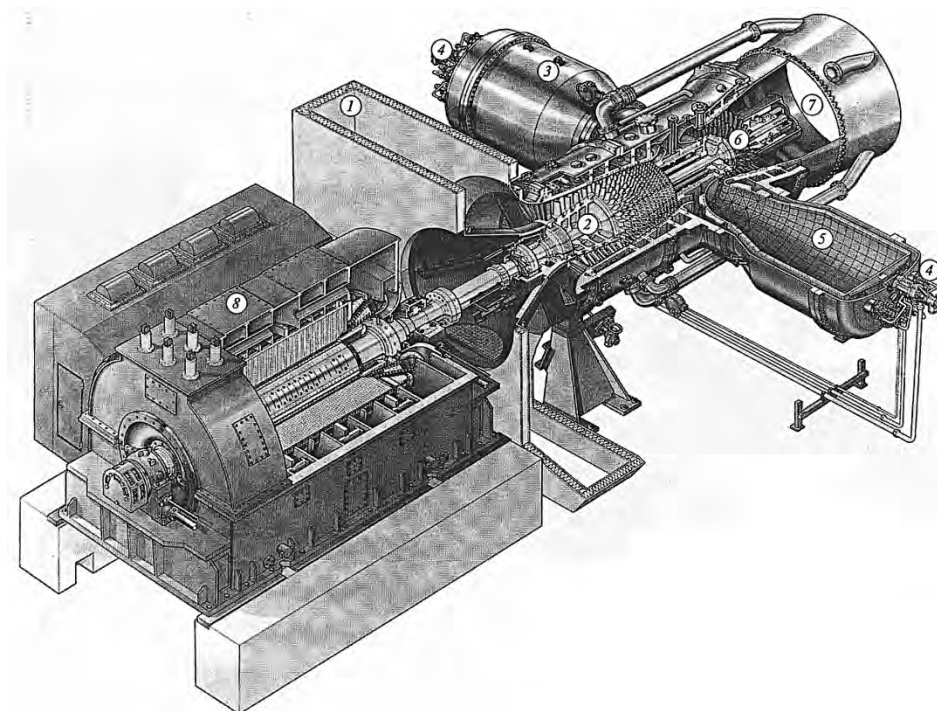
Пример компоновки выносных КС энергетической ГТУ (V94.3 фирмы Siemens): 1 — свежий воздух; 2 — компрессор; 3 — камера сгорания; 4 — горелка, 5 — пламенная труба и впускная коробка горячих газов; 6 — турбина; 7 — отходящий газ газовой турбины; 8 — генератор.
